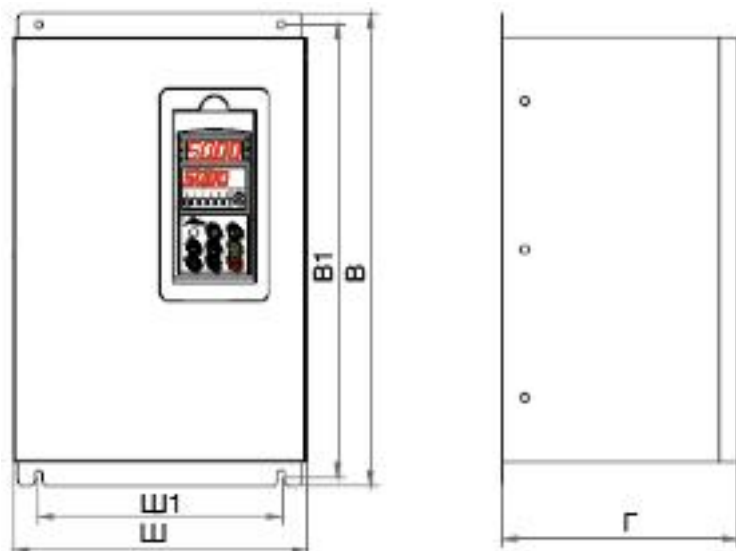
Габаритный чертеж преобразователя частоты модели В
